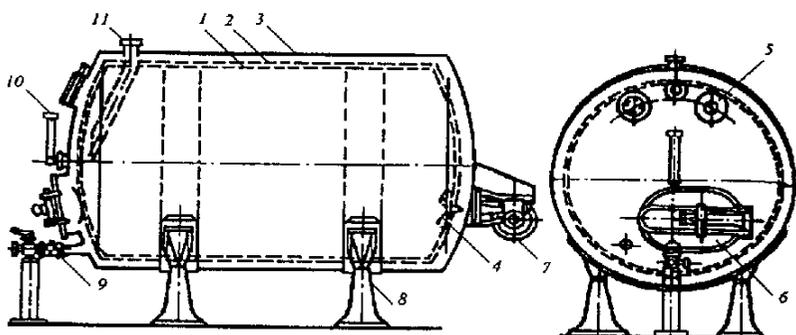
Горизонтальный резервуар для хранения молока: 1 - рабочий резервуар; 2 - теплоизоляция; 3 - кожух; 4 - мешалка; 5 - смотровое окно; 6 - люк; 7 - привод мешанки; 8 - опорные ножки; 9 - сливной патрубок; 10 - термометр; 11 - наливная труба
